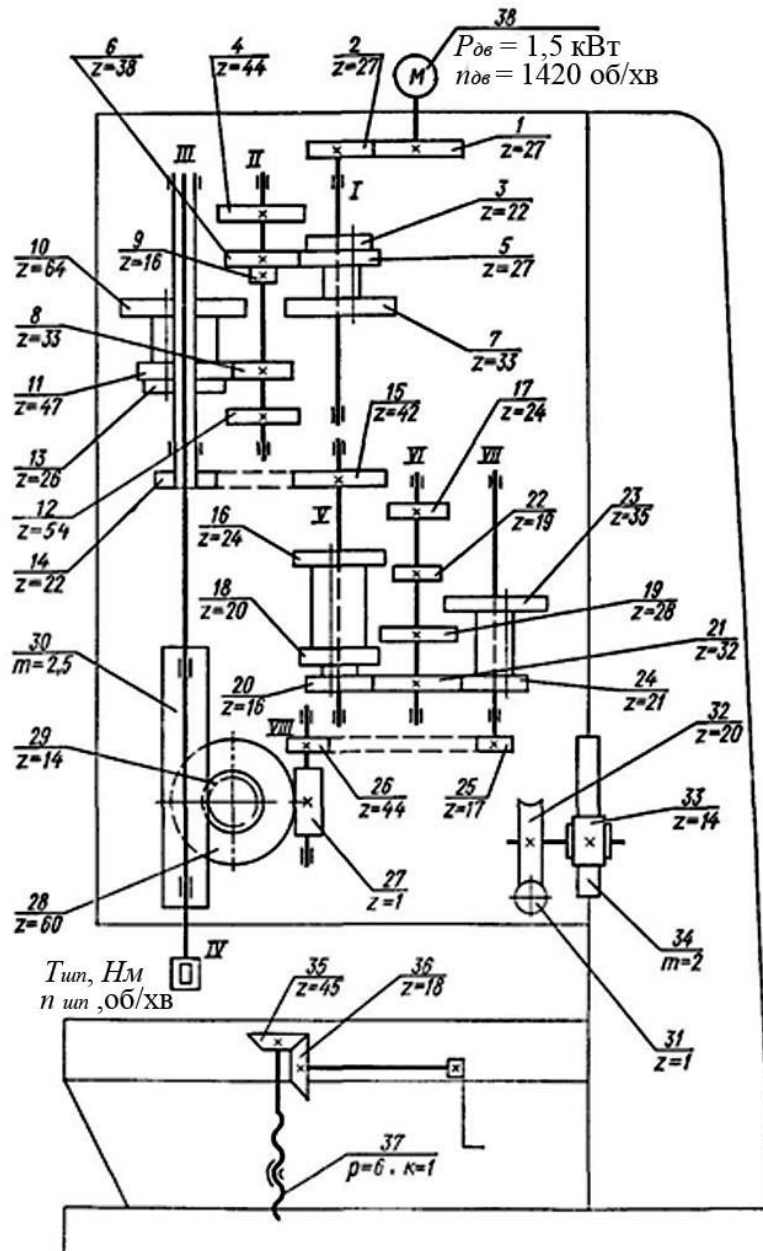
Кінематична схема вертикально-свердлильного верстату 2Н118
